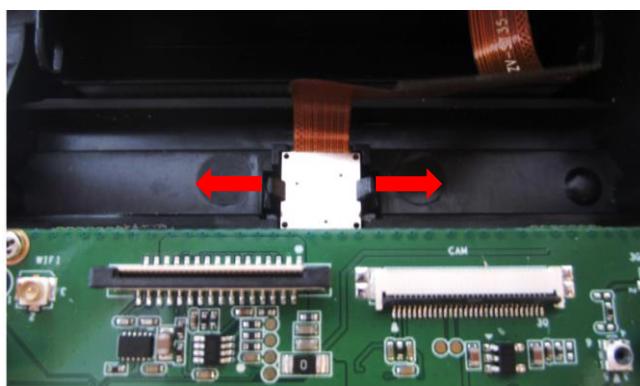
Демонтаж камеры из корпуса верхнего.
